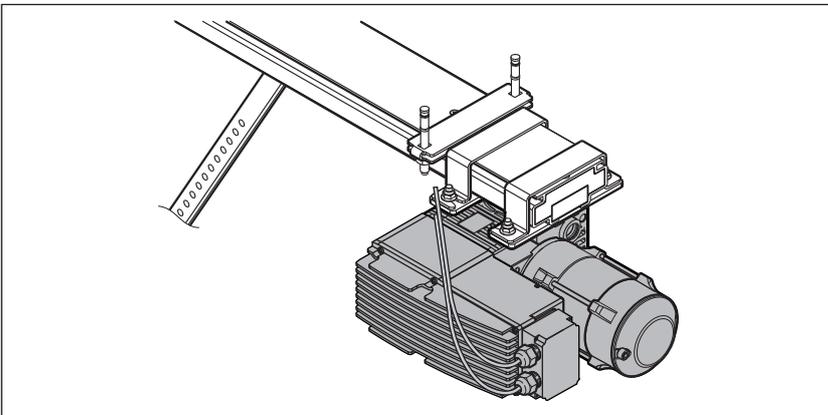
Montageart Schienengeführter Antrieb ITO
